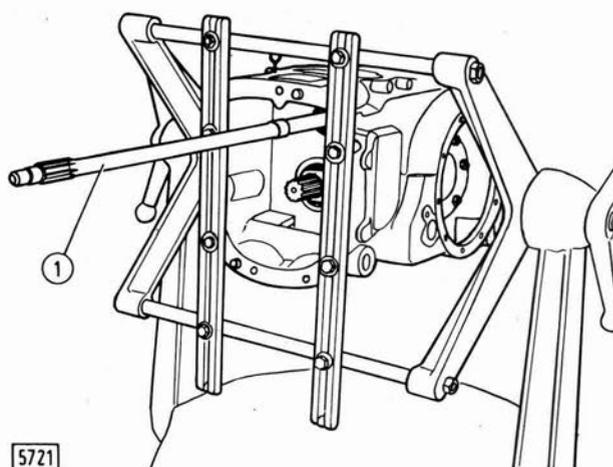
Carter de transmission arrière monté sur le chevalet rotatif ARR 2220.
